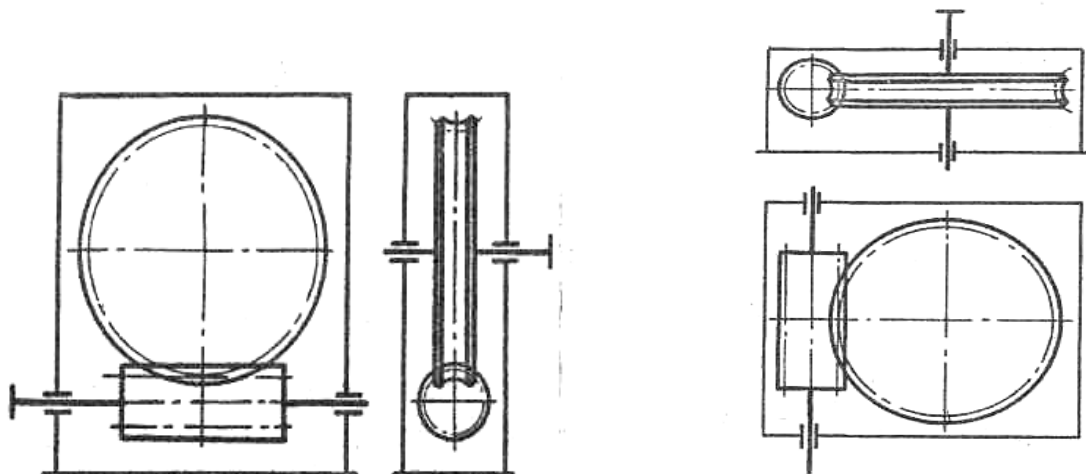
Схема червячного редуктора с горизонтальным расположением червяка под колесом (редуктор типа РЧП)
